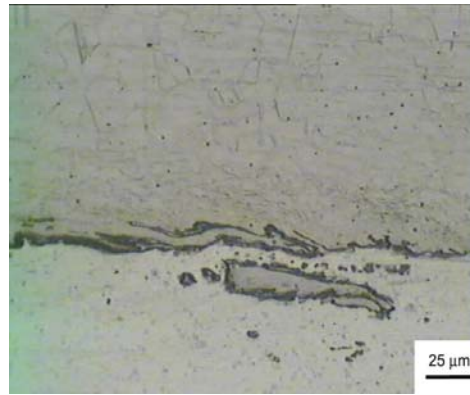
Zona defectuosa de la soldadura Al-SS producida por el contacto del extremo del pin con el SS.
